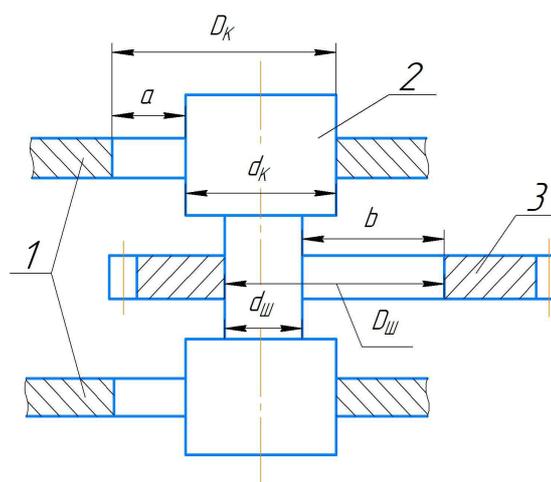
Схема критического положения деталей узла промежуточной шестерни:
